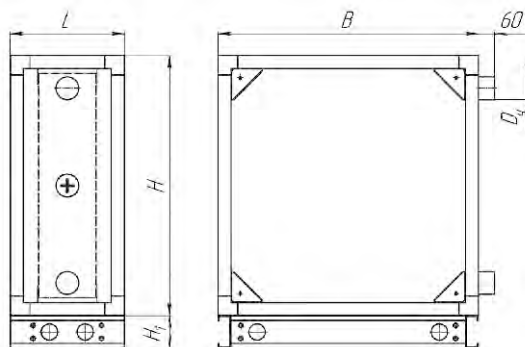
Габаритные размеры. Блок воздушонагревателя парового.
